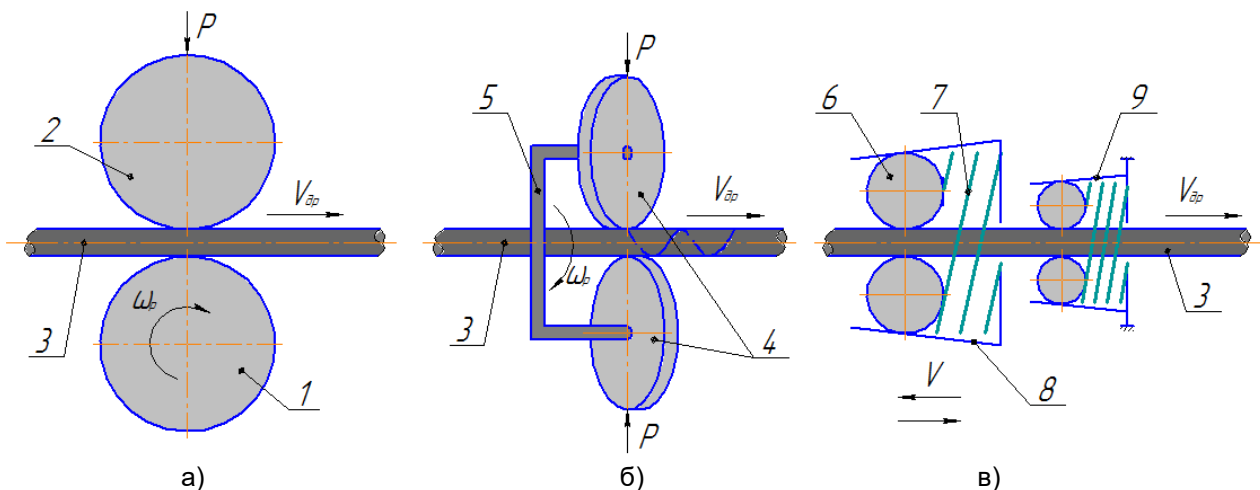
Схеми механізмів подачі зварювальних апаратів
